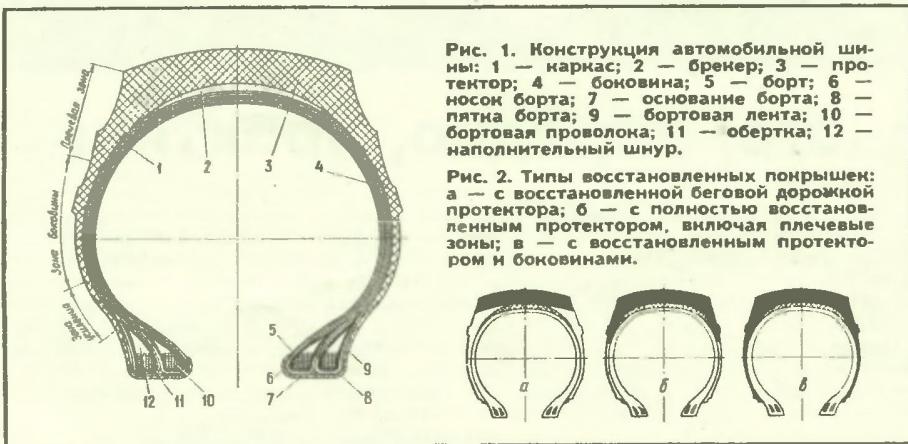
Конструкция автомобильной шины: 1 — каркас; 2 — бранкер; 3 — протектор; 4 — боковина; 5 — борт; 6 — носок борта; 7 — основание борта; 8 — пятка борта; 9 — бортовая лента; 10 — бортовая проволока; 11 — обертка; 12 — наполнительный шнур.
